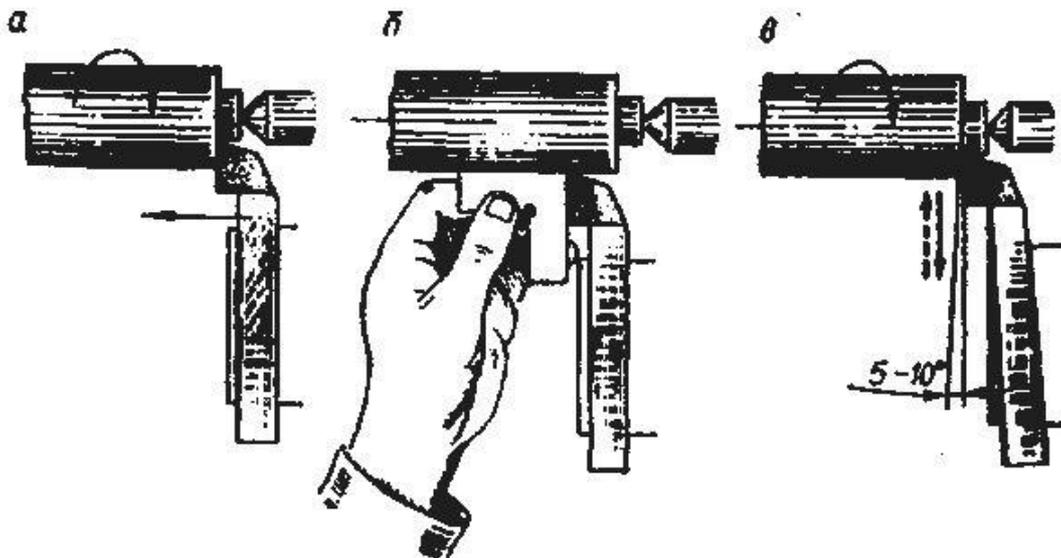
Положение резцов при обработке ступенчатых поверхностей
